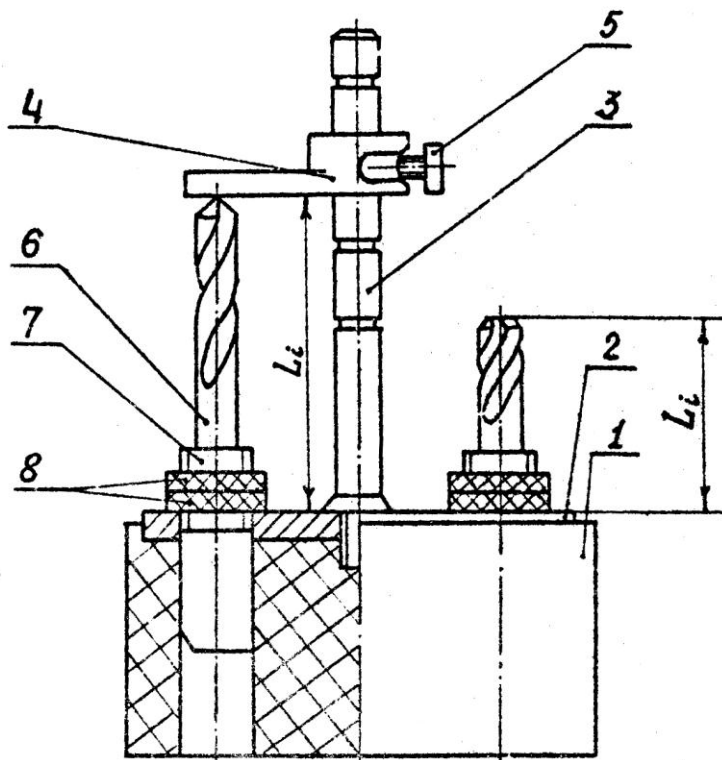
Прибор флажкового типа: 1 – корпус; 2 – плита; 3 – стойка; 4 – подвижный флажок; 5 – винт; 6 – осевой инструмент; 7 – оправка; 8 – контргайки
